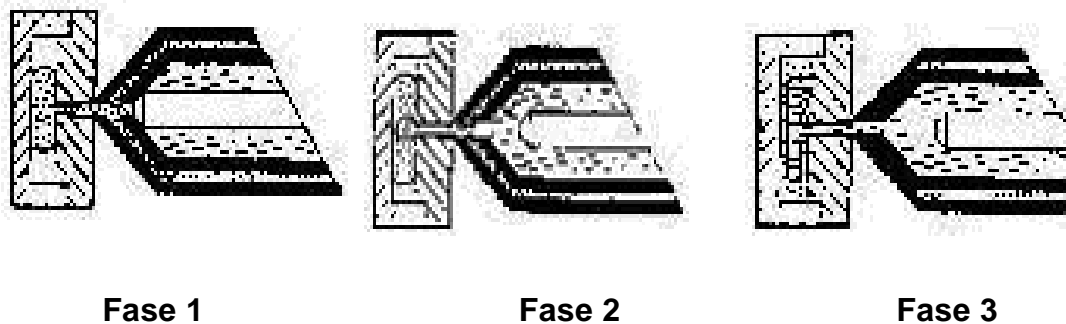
Inyección de materiales múltiples a través de una boquilla única.
